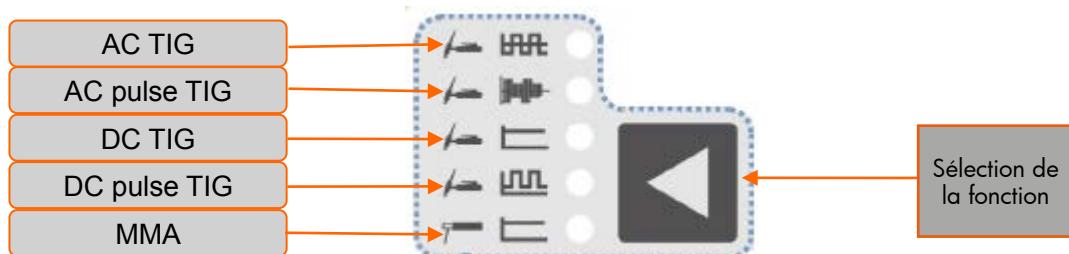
Panneau de sélection du mode de soudage
